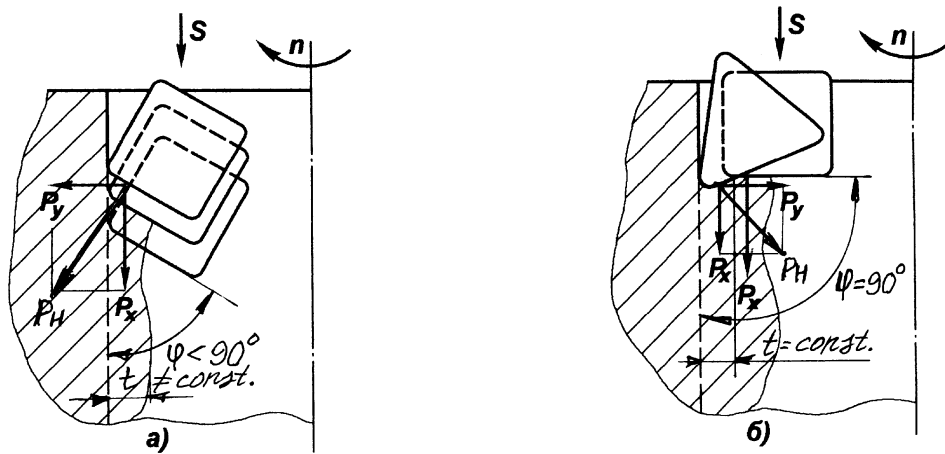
Схема удаления припуска на операции черного растачивания отверстия цилиндрической заготовки
